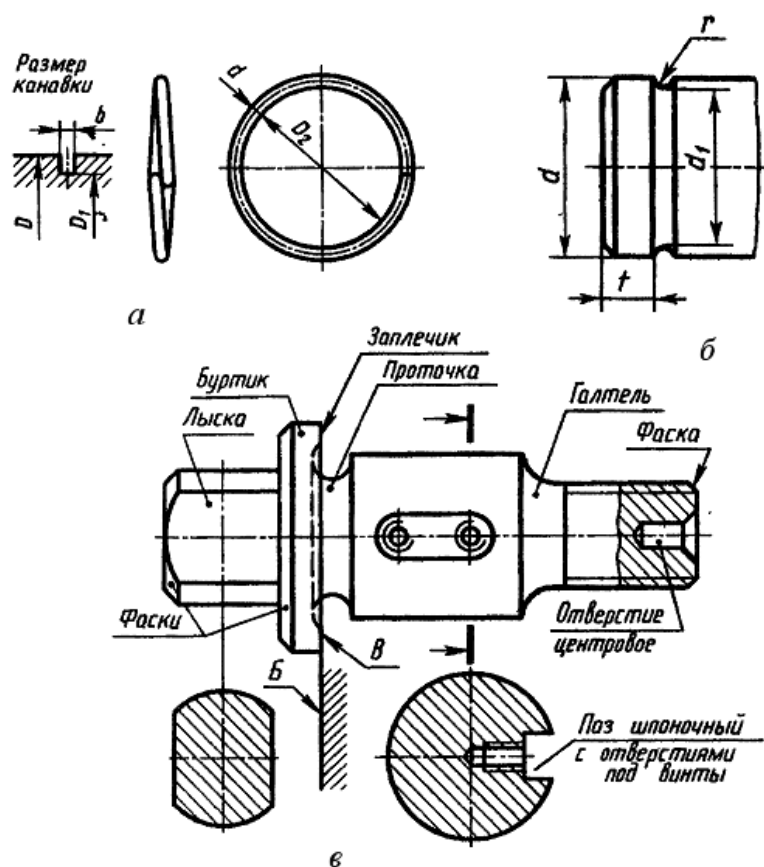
Конструктивные элементы деталей: канавка (а); проточка (б); паз, лыска, запечник, галтель, буртик (в)
